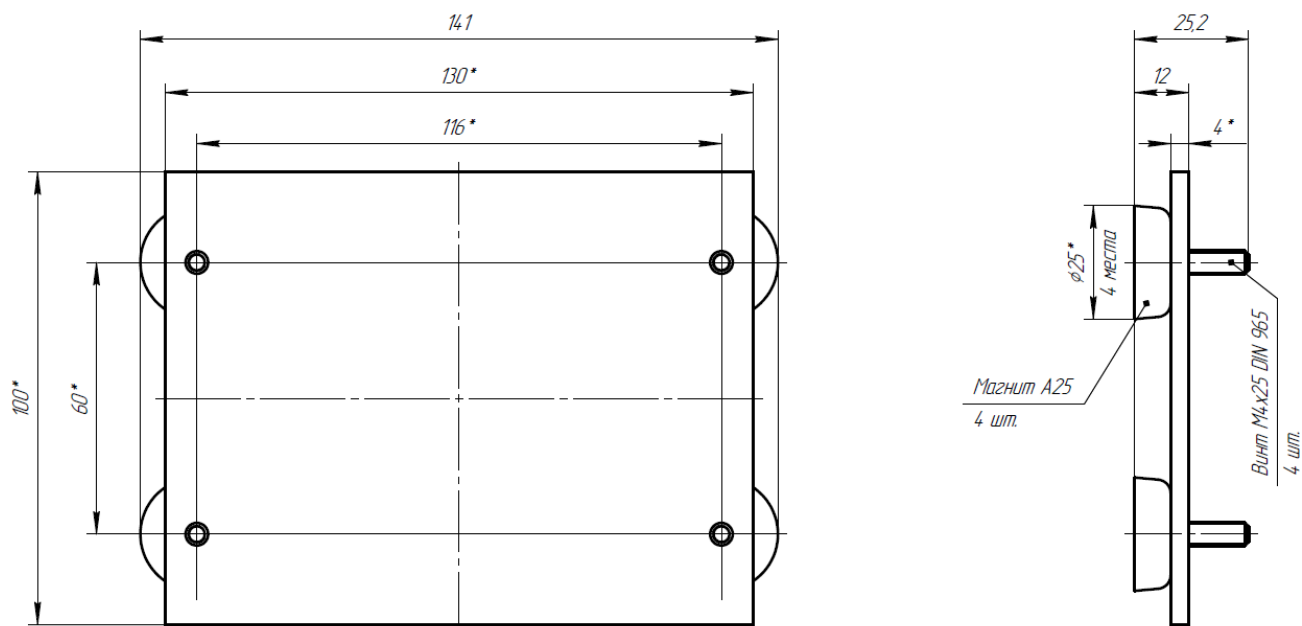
Монтажный чертеж установки пластины на вертикальную поверхность
